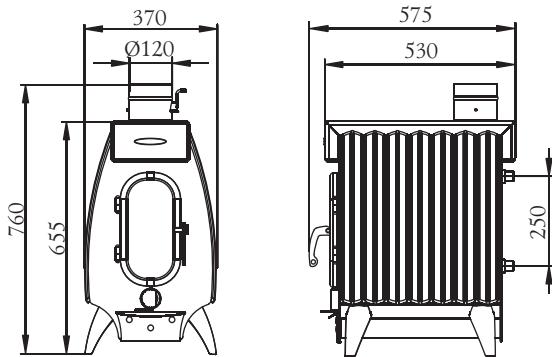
Габаритные размеры «Огонь-батарея 7Б Лайт».
